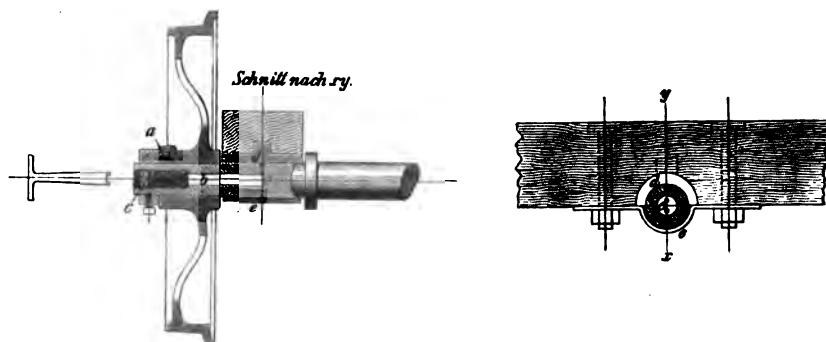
und 352. Schmierzvorrichtung auf Zeche Fortschritt bei Dux in Böhmen.
